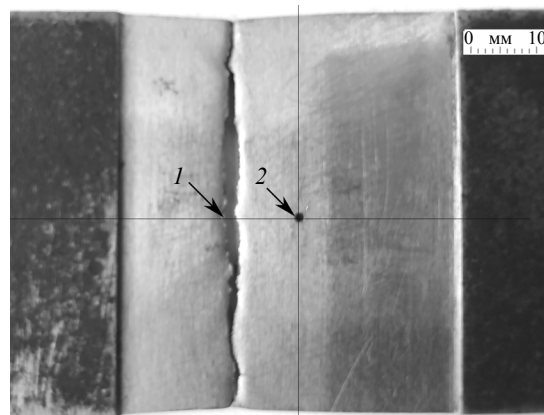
Разрушение образца СШ-3 в зоне термического влияния сварного шва:
